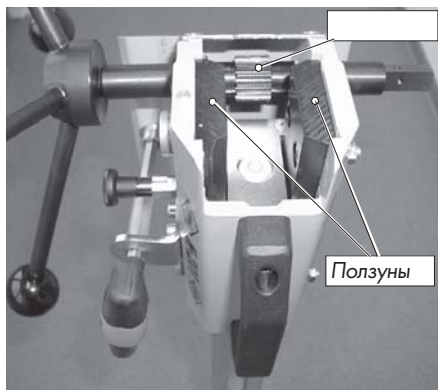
Салазки Н•201 над зубчатой рейкой направляющей (вал привода свободен)
